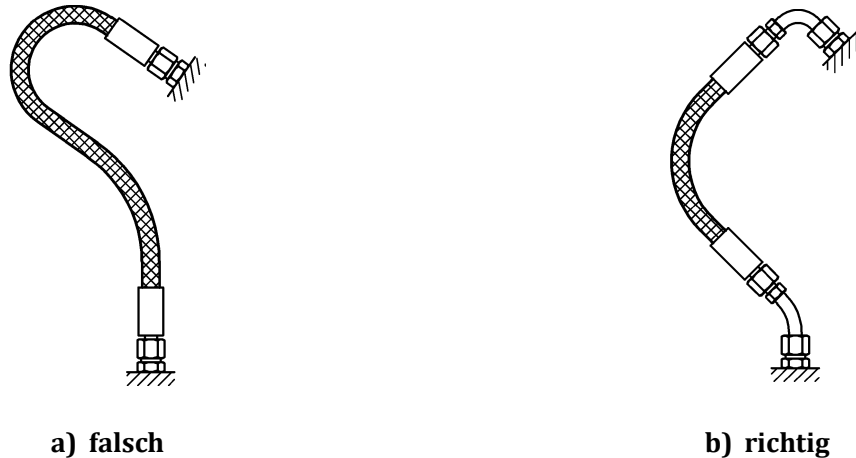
Einbau mit bzw. ohne Bogenarmatur
